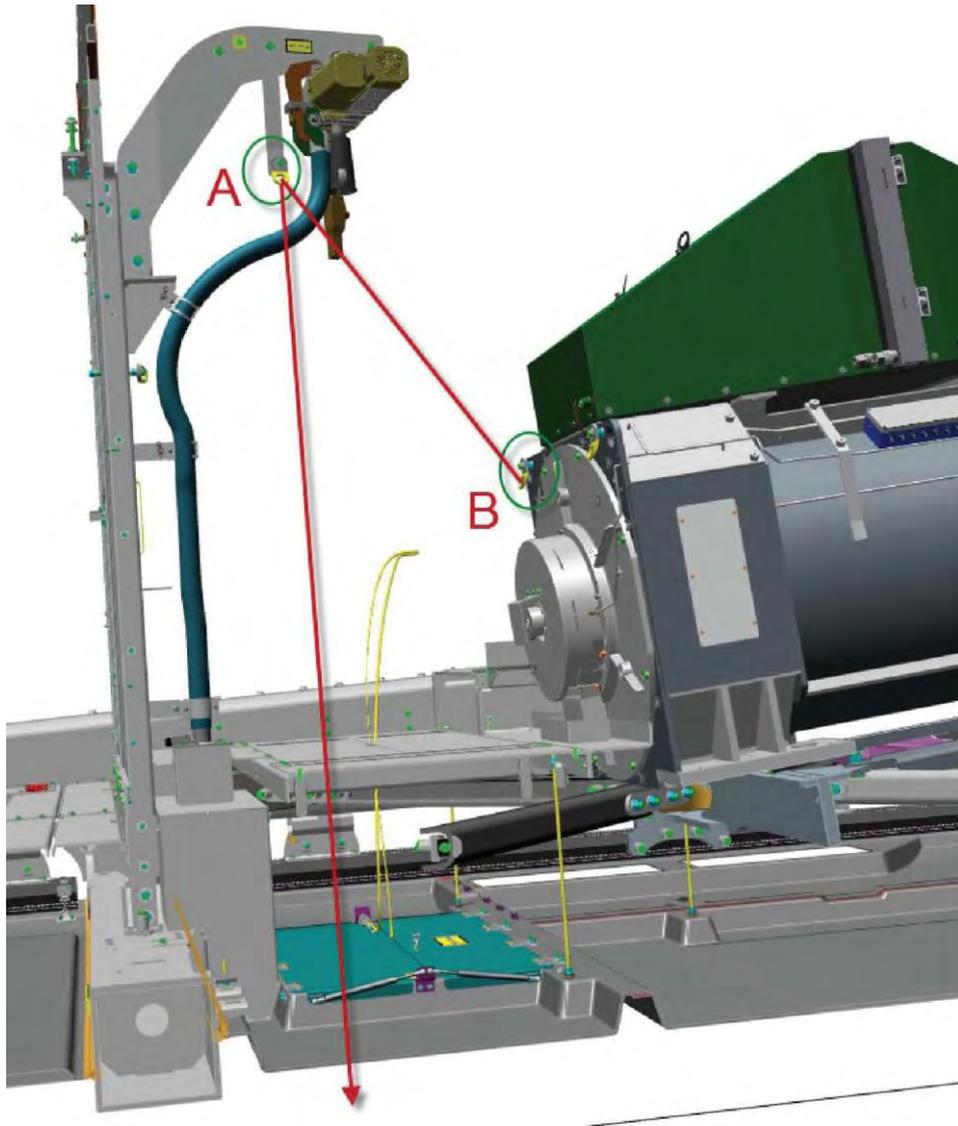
Rettungsroute im Maschinenhaus (Detailansicht)
